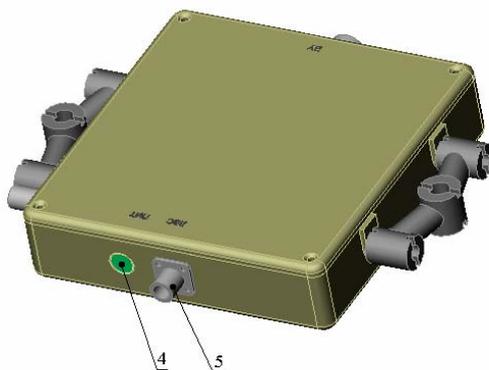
Габаритные чертежи блока сопряжения МСЗ
